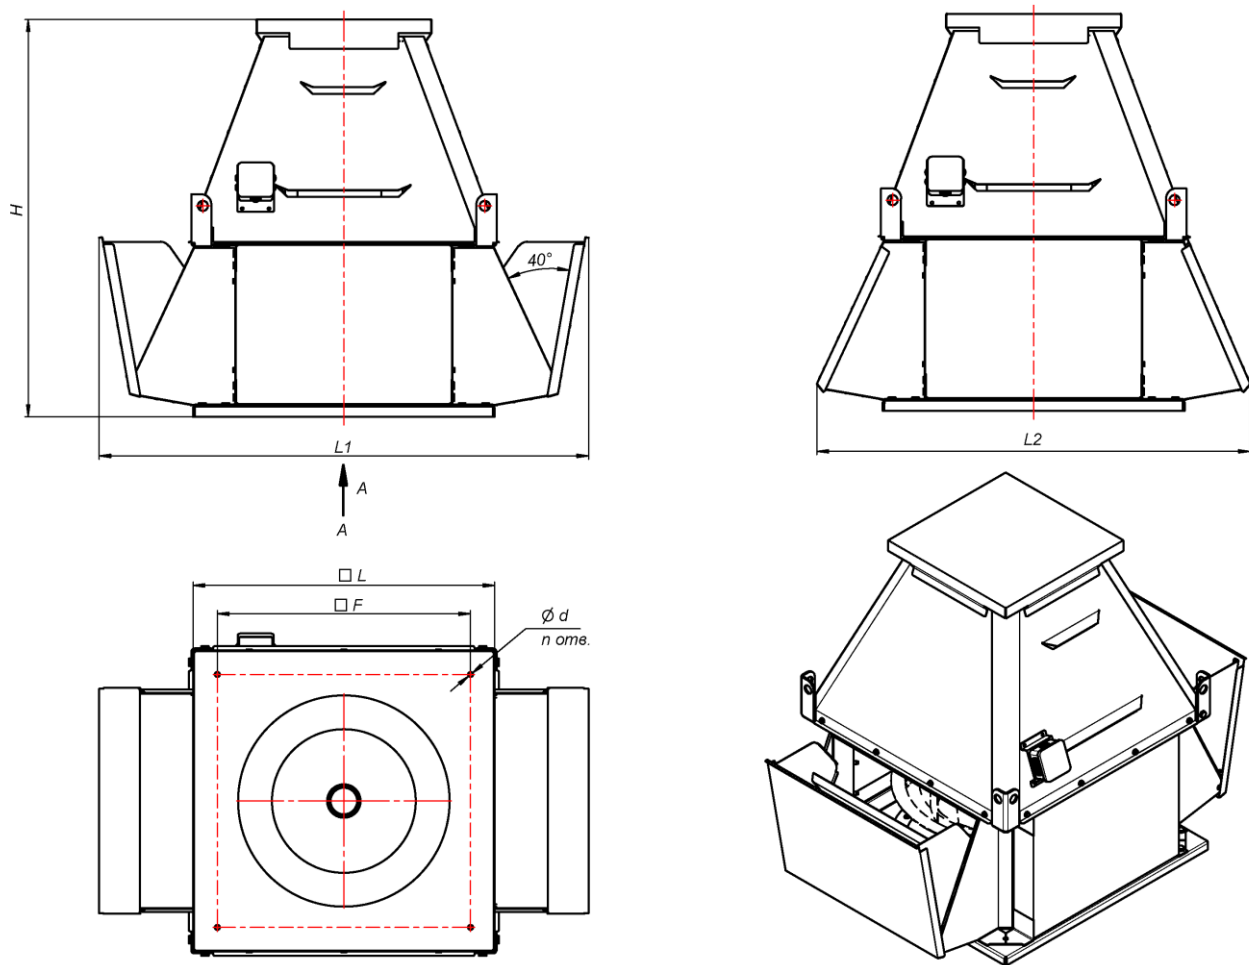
Габаритные, присоединительные размеры и общий вид вентиляторов RAW
